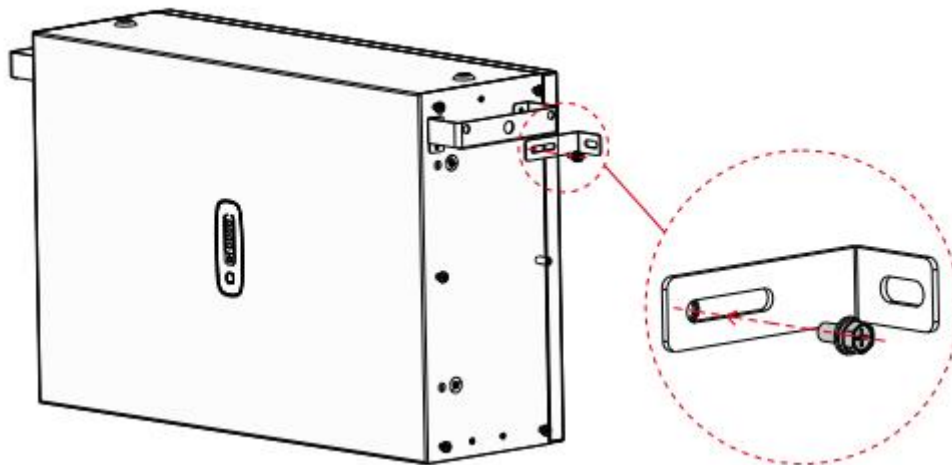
Installazione della Staffa per Montaggio a Parete
